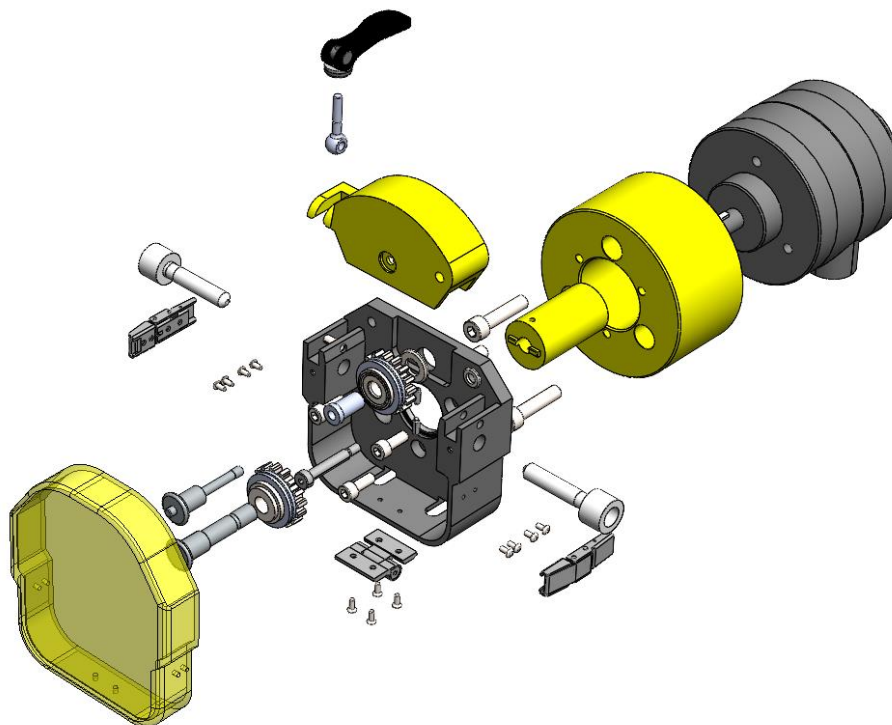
Vista explodida do sistema de alimentação de fio de soldadura
